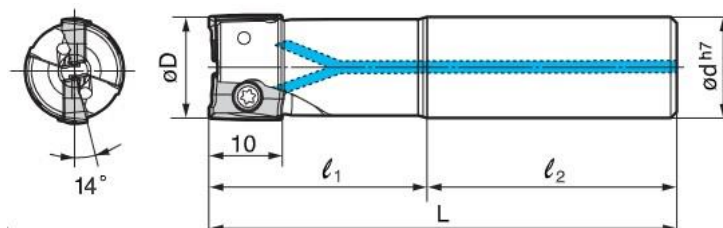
Кінцева фреза зі змінними пластинами Корпус WEX 2014 E [1, с. 214]
